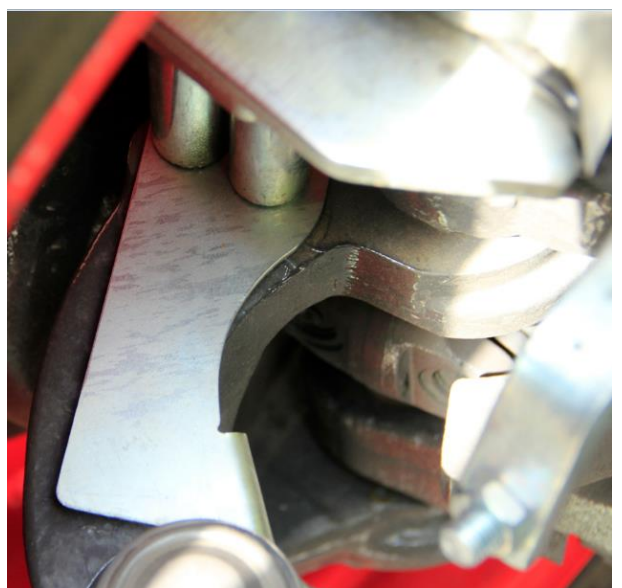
Bügel ist mit 2 Schrauben an der Stütze des Kotflügels befestigt.
